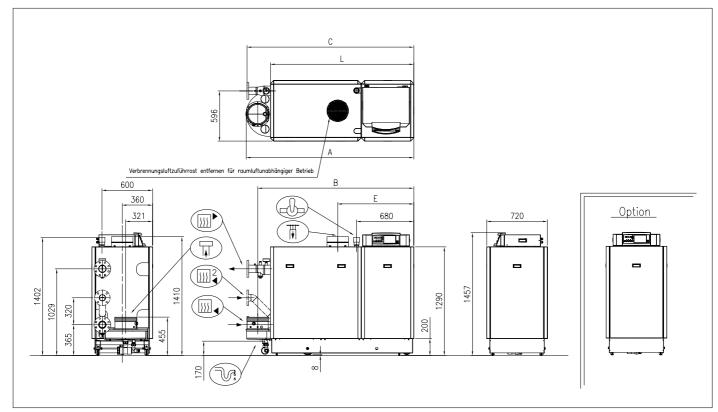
Ansichtszeichnungen (dargestellt ist die Linksausführung) 05.31H.79.00001
